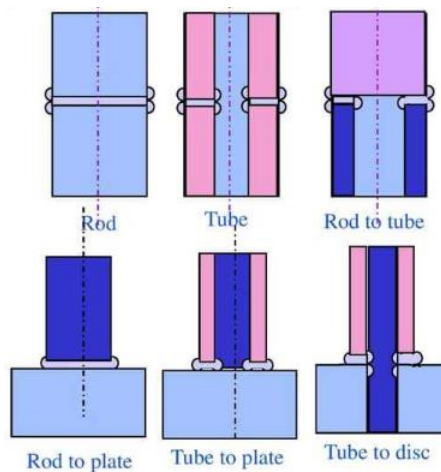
Inertia-Drive Friction Welding
